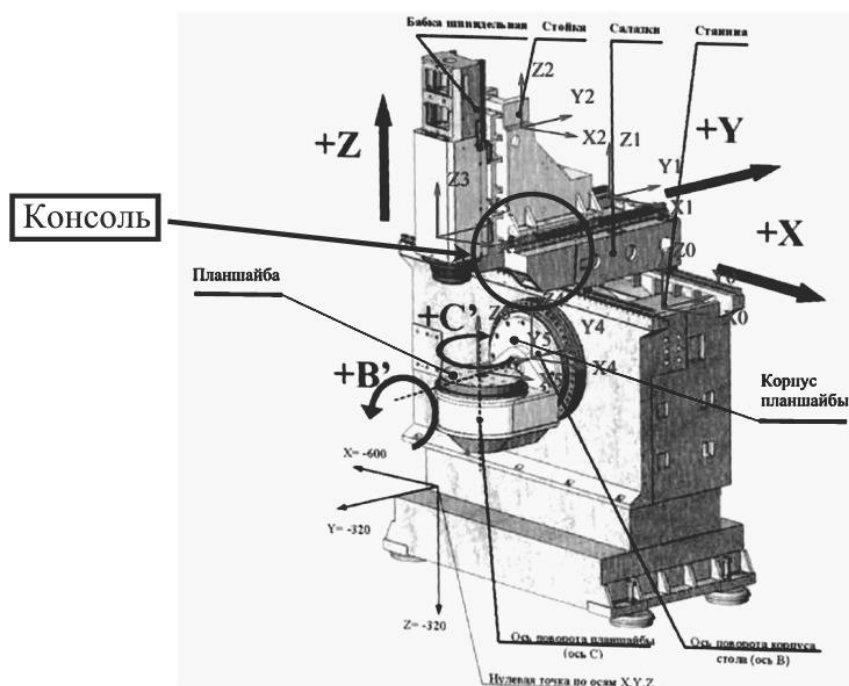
Конструкция станка мод. МС – 300 с салазками консольного типа
